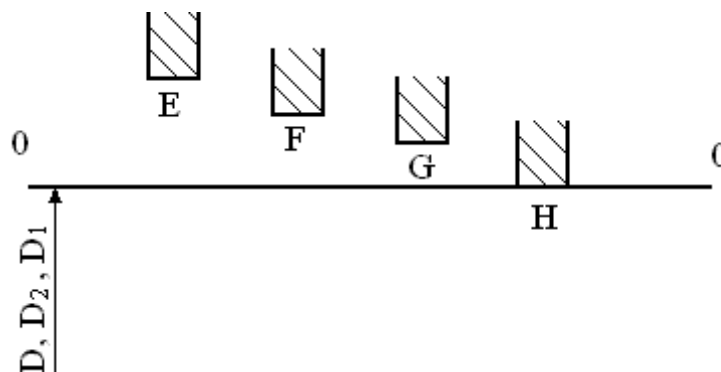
Основные отклонения для резьбы гайки (посадка с зазором)
